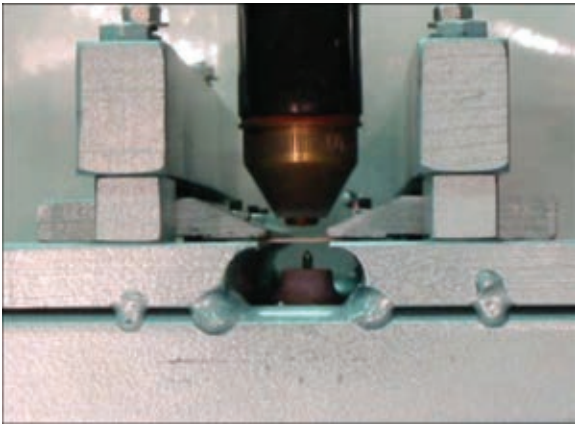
Двухсторонняя плазменно–дуговая сварка и сварка неплавящимся электродом [32]
